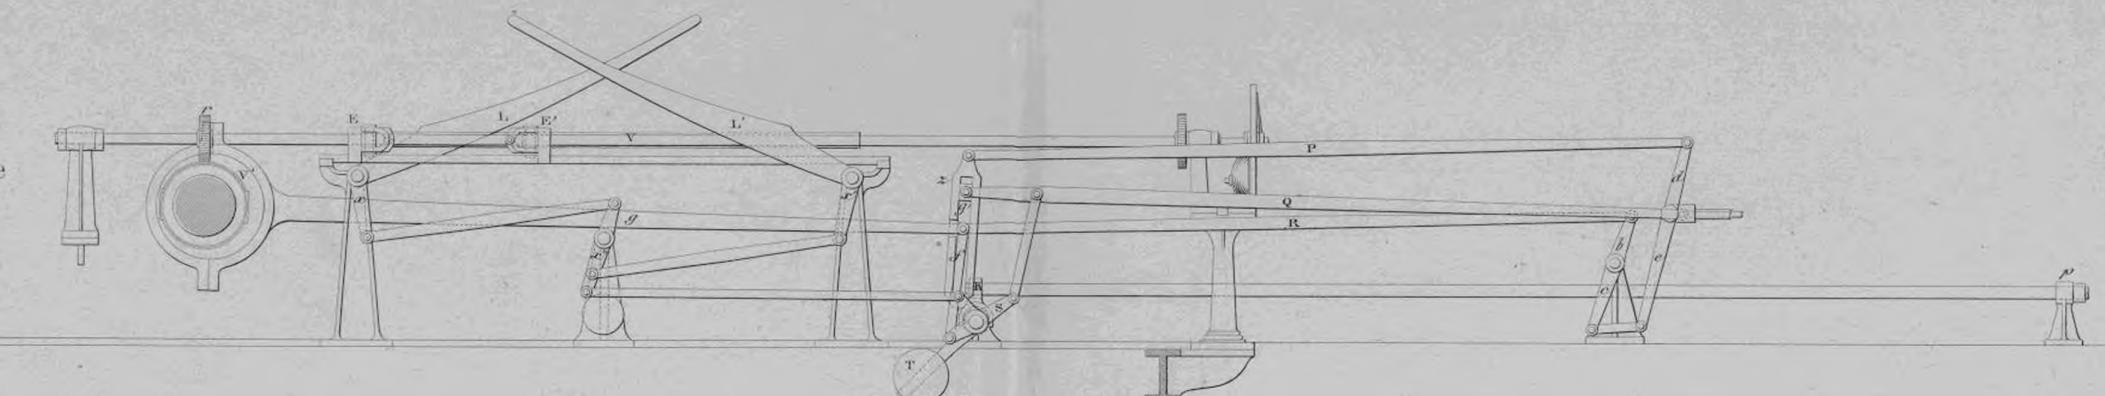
PLAN DE LA CHAÎNE FLOTTANTE.
